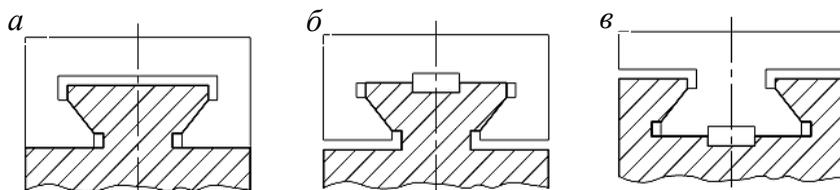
Типы направляющих скольжения базовых деталей с трапецидальным профилем, типа ласточкина хвоста, с охватываемыми (а, б) и охватывающими (в) поперечными сечениями
